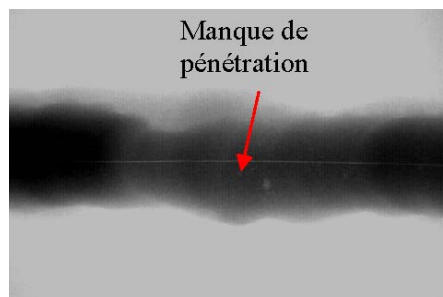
Radiographie d'une soudure d'aluminium
